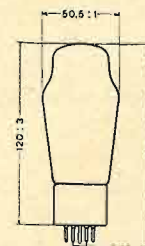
Dimensioni d'ingombro della valvola 5R4GY.
